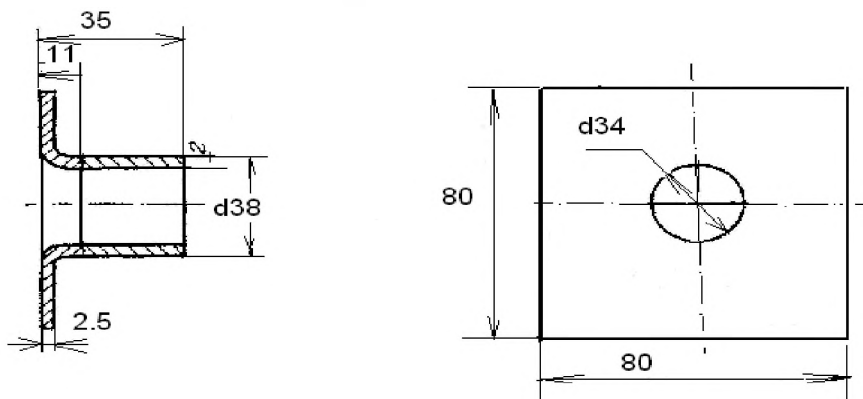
Зразки для досліджень стикового зварного з'єднання труби з тонкими решітками.
